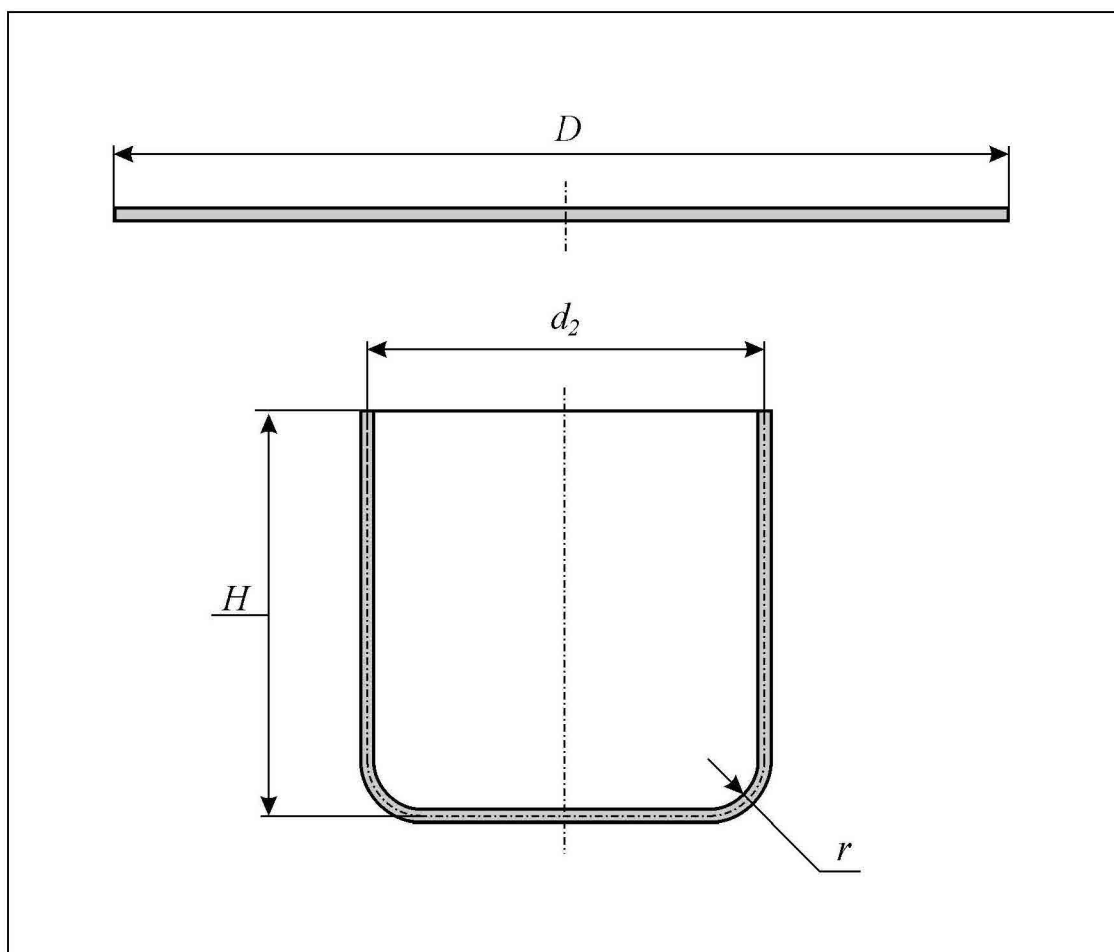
До розрахунку діаметра вихідної заготовки
